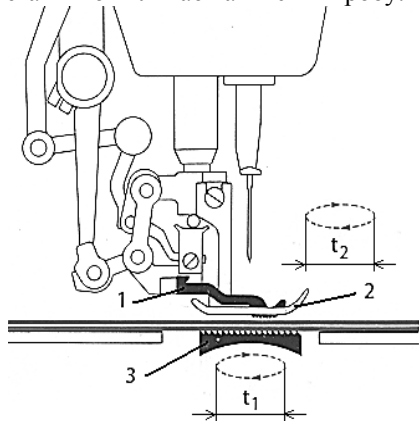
Конструкція механізму транспортування ускладнена: 1 – верхній зубчатий транспортер; 2 – притискаюча лапка; 3 – нижня зубчата рейка
